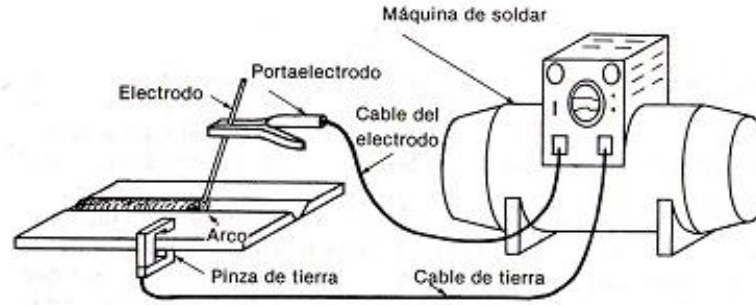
Elementos básicos de la soldadura de arco.
